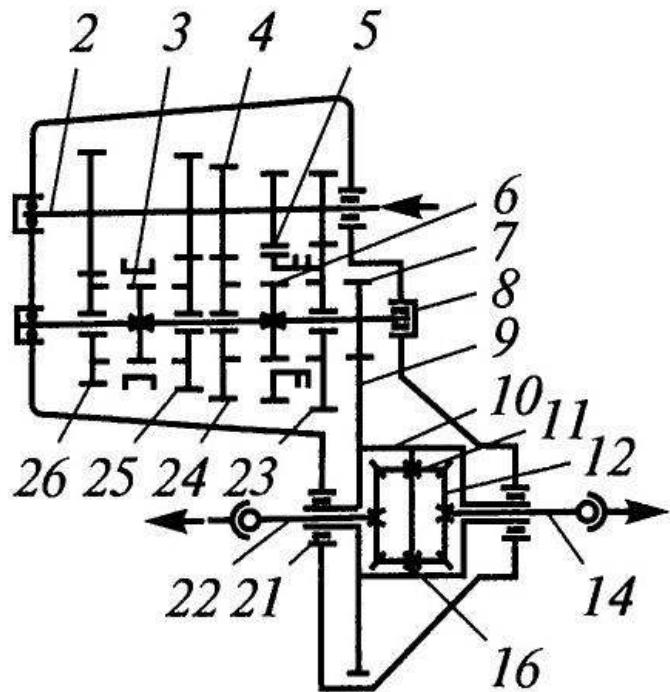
Кинематическая схема коробки передач автомобиля ВАЗ:
